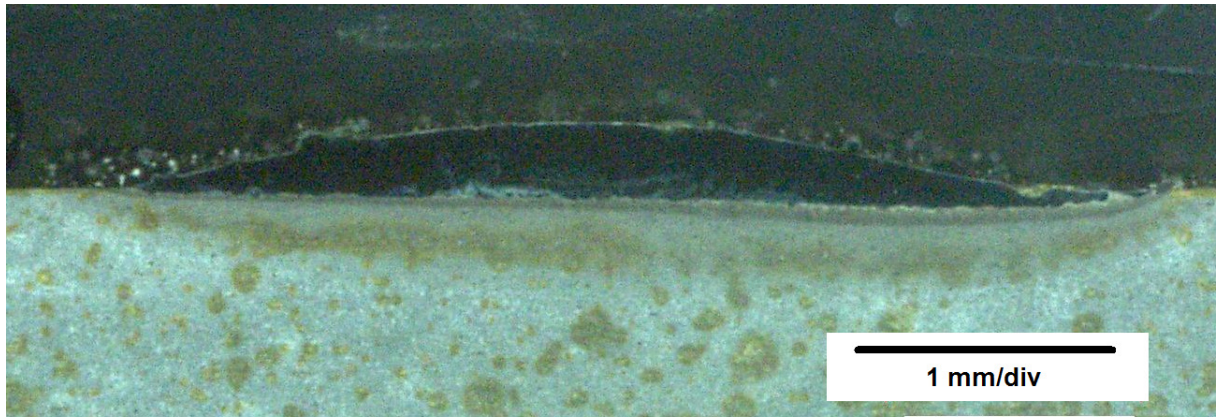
Querschliff einer Auftragschweißspur die mit $f_2=200$ mm bei hoher Laserleistung P_L und hohem Pulvermassenstrom \dot{m} aufgetragen wurde
